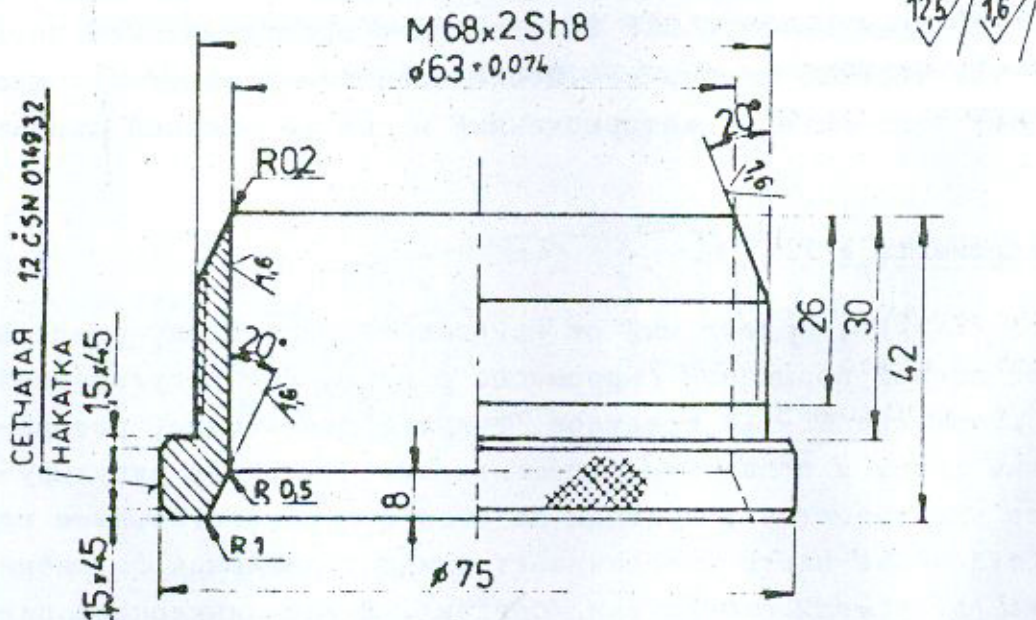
Приспособление для монтажа поршня в прямолинейный гидродвигатель
